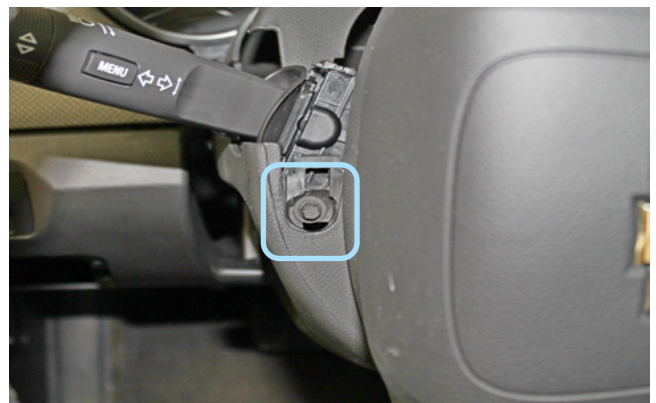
Саморез крепления нижней части кожану рулевого вала слева
